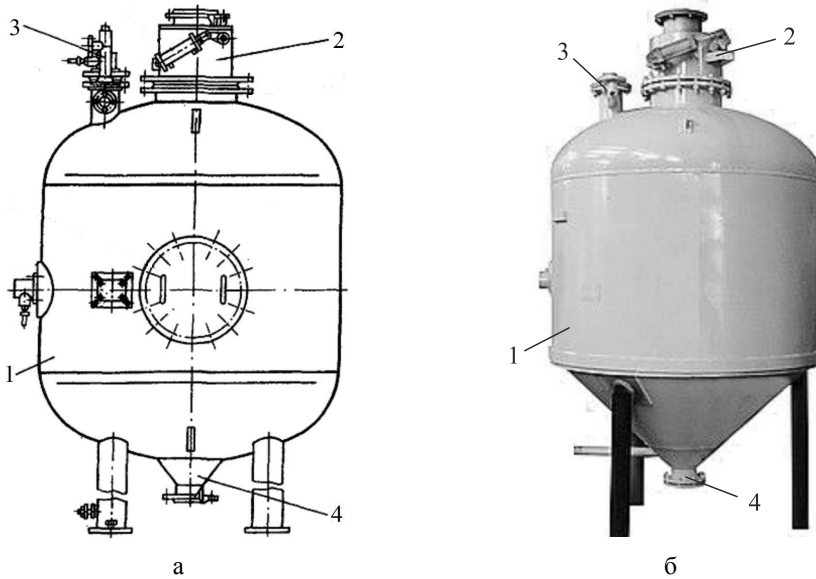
Бак передувочний з еліптичним (а) і конічним (б) днищем: 1 — циліндрична ємність; 2 — затвор; 3 — патрубок подачі стиснутого повітря; 4 — розвантажувальний конус
